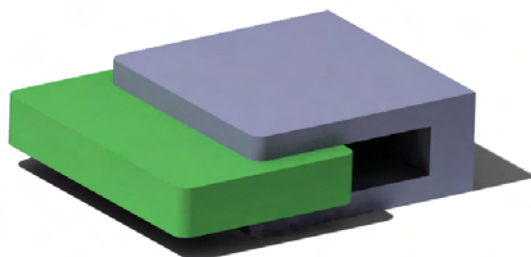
Vue 3D d'une liaison appui plan bilatérale entre la pièce grise et la pièce verte
